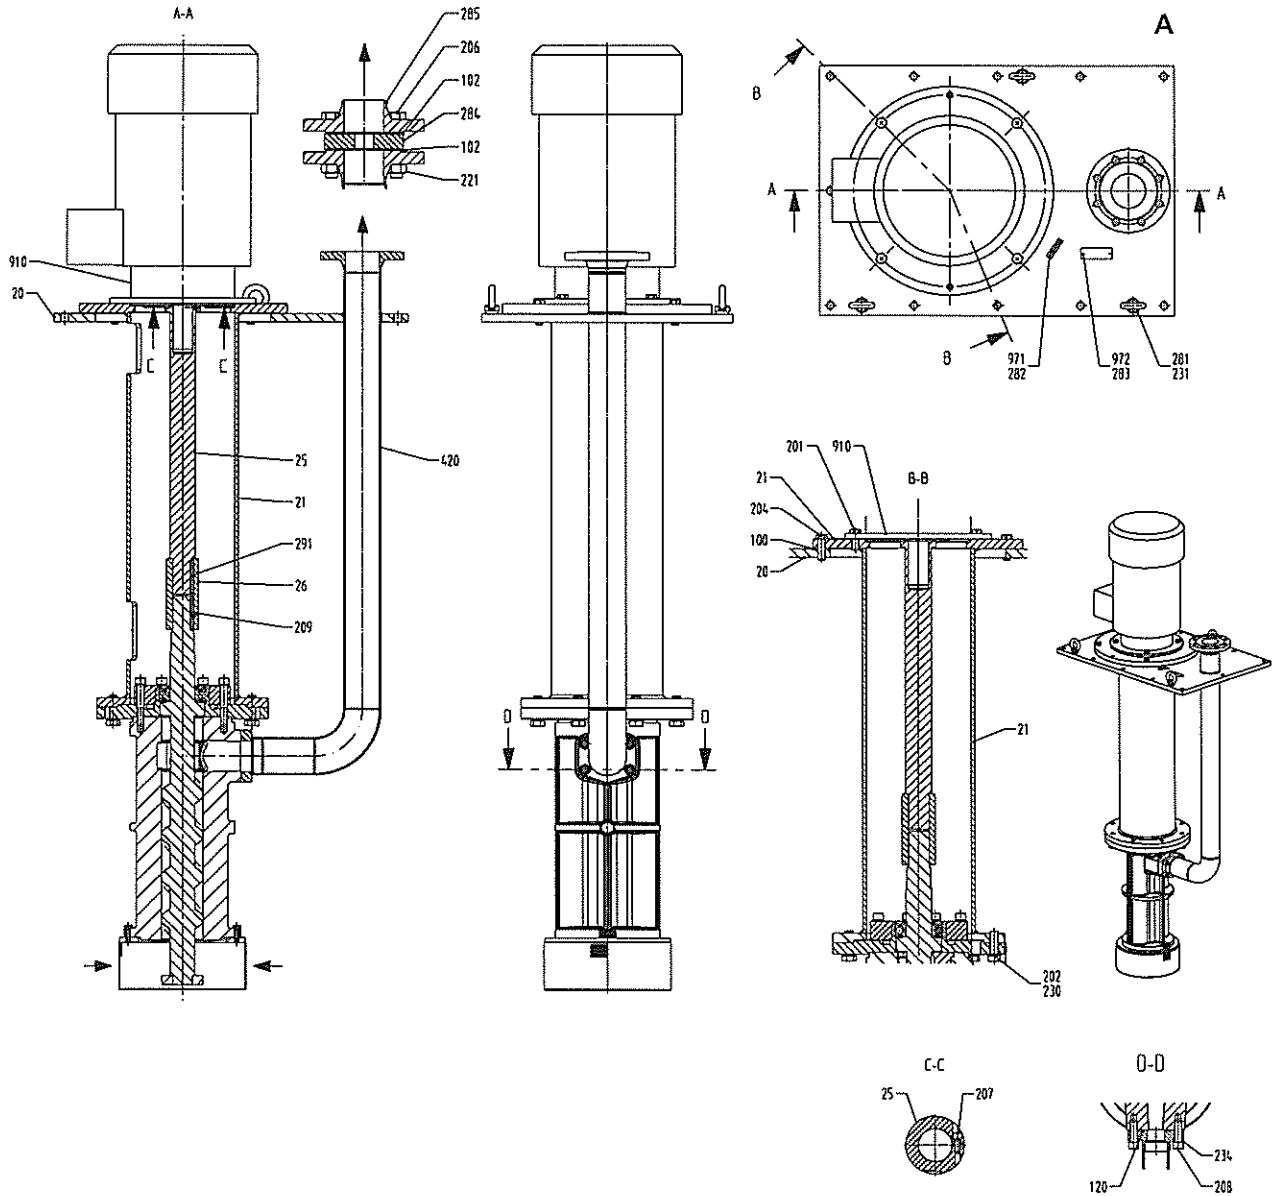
Исполнение с соединителем и вставным валом, BG 660/940/1300
